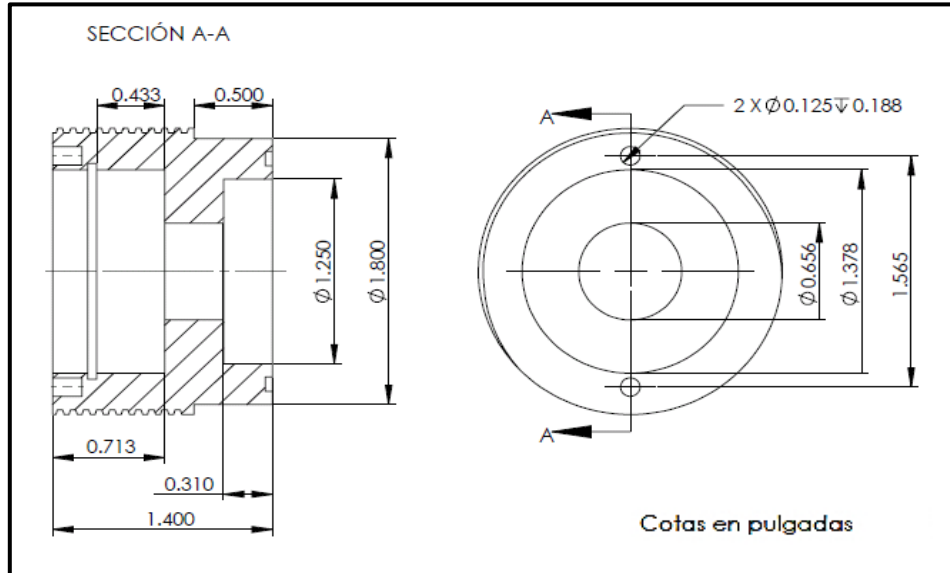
Dimensiones del portasello mecánico primera parte.
